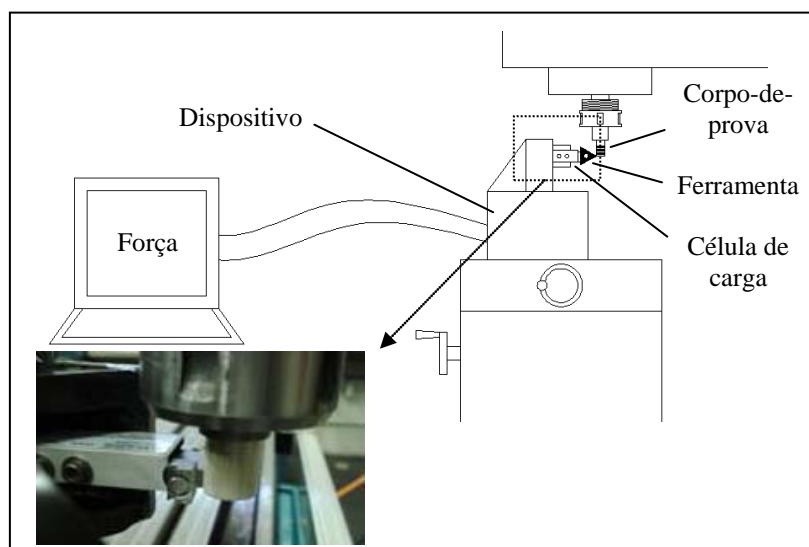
Montagem esquemática do banco de ensaio de usinagem
